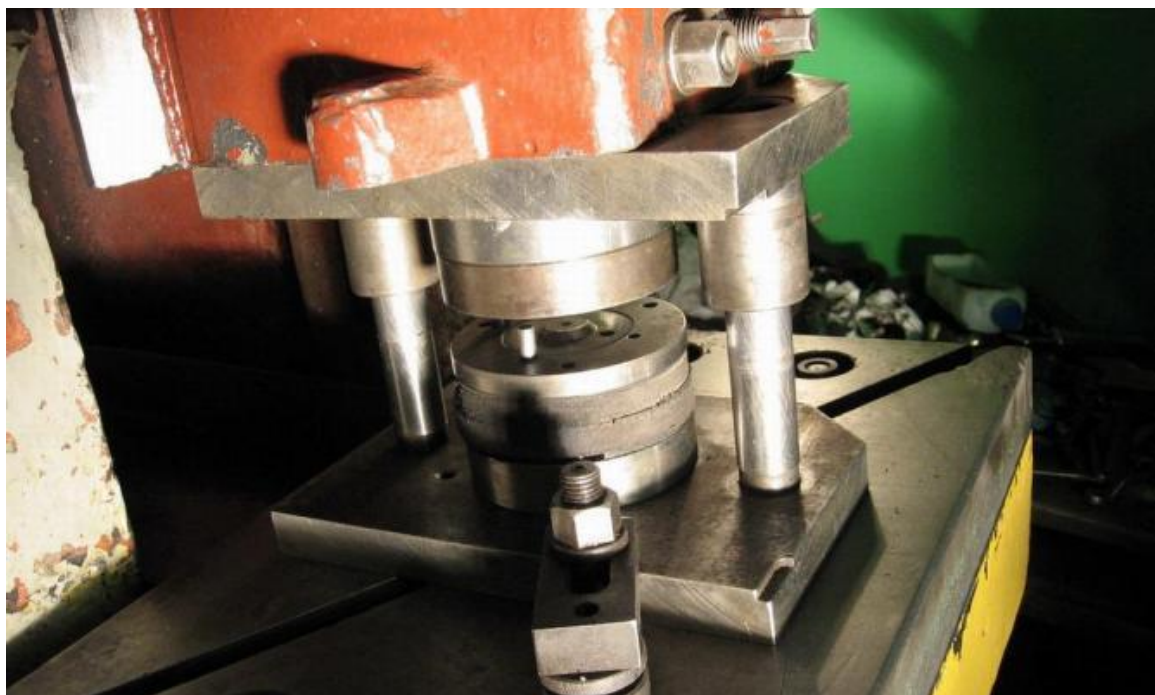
Изготовление деталей при помощи высокого давления
